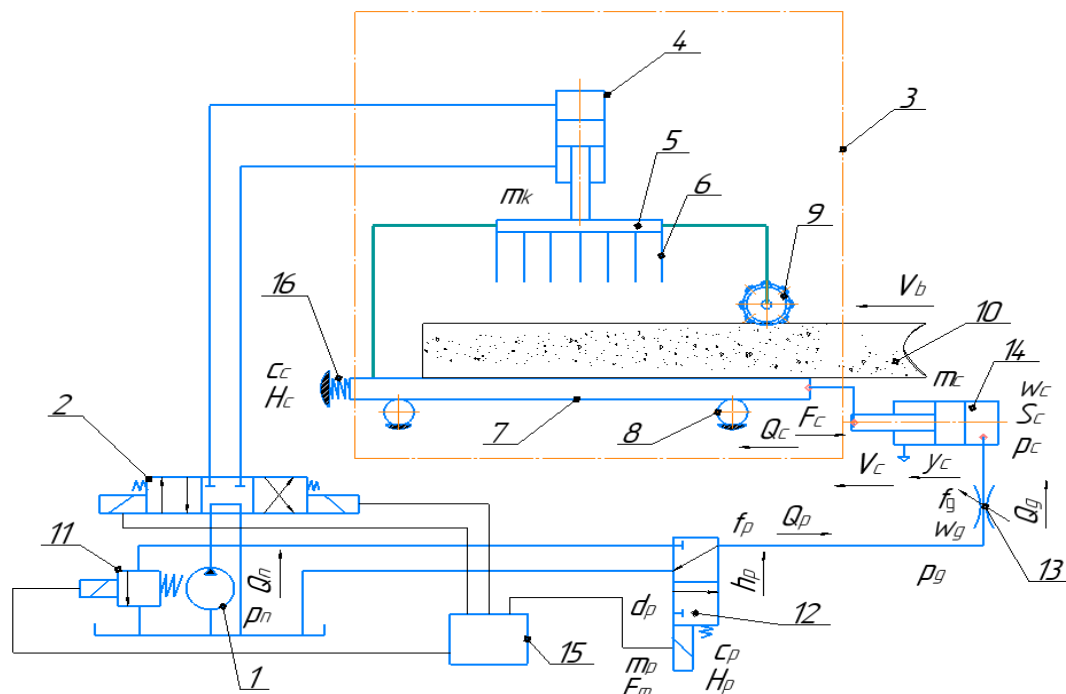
Гідравлічна схема установки для формування заготовки цегли
